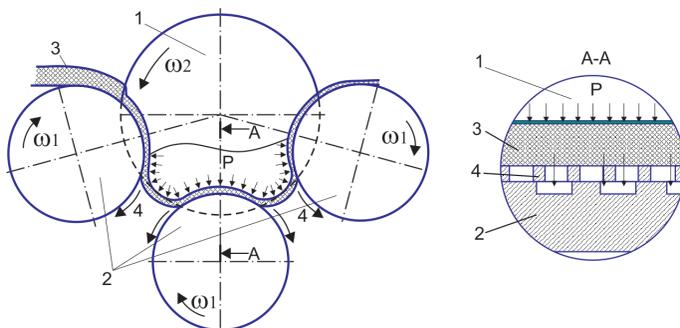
Схема рабочих органов разработанной конструкции пресса:
